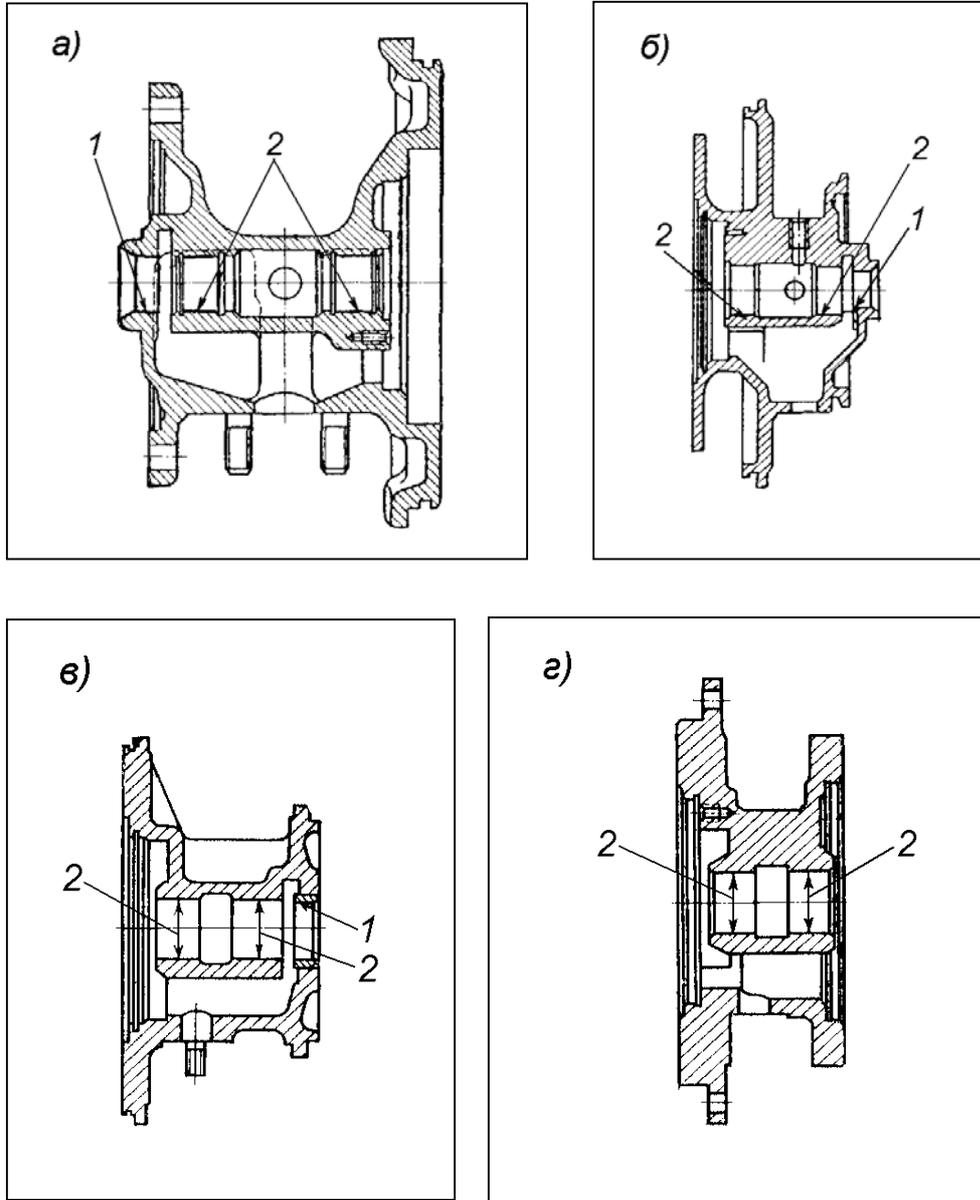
а) – корпус подшипников ТКР-11 ЯМЗ; б) – корпус подшипников ТКР-9 ЯМЗ;
